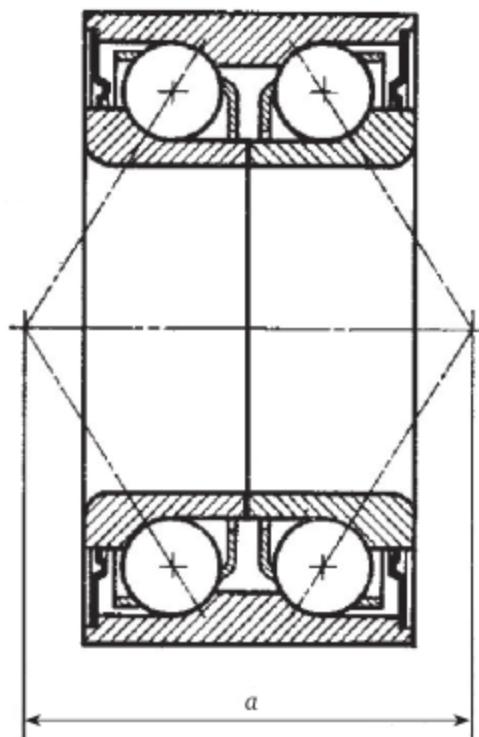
Двухрядный радиально-упорный шариковый подшипник с разрезным внутренним кольцом:
